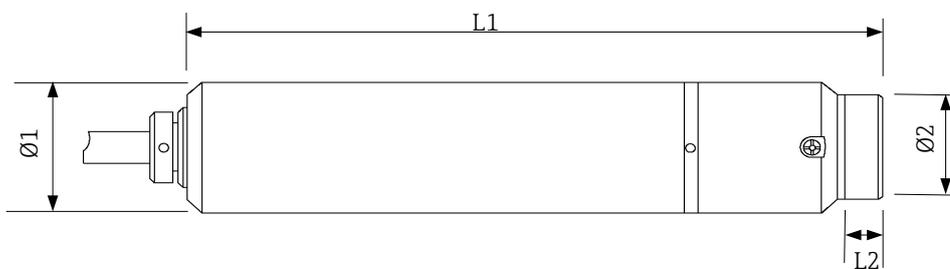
Dimensioni sonda Rxn-20 e adattatore per lenti
